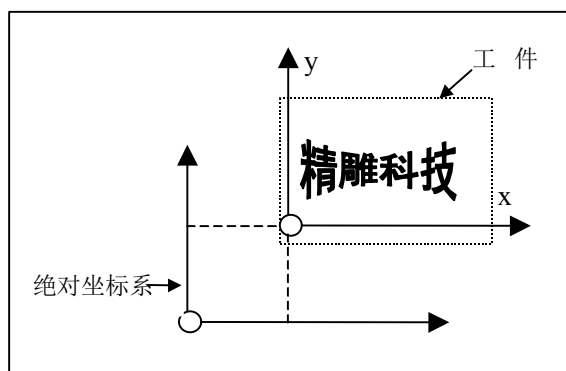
工件原点在绘图坐标系的位置就是输出原点
